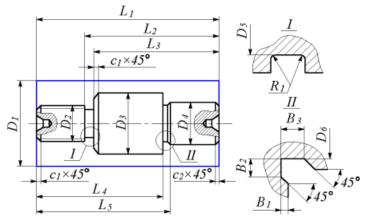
Эскиз обрабатываемой детали для вариантов 1, 6, 11, 16, 21
